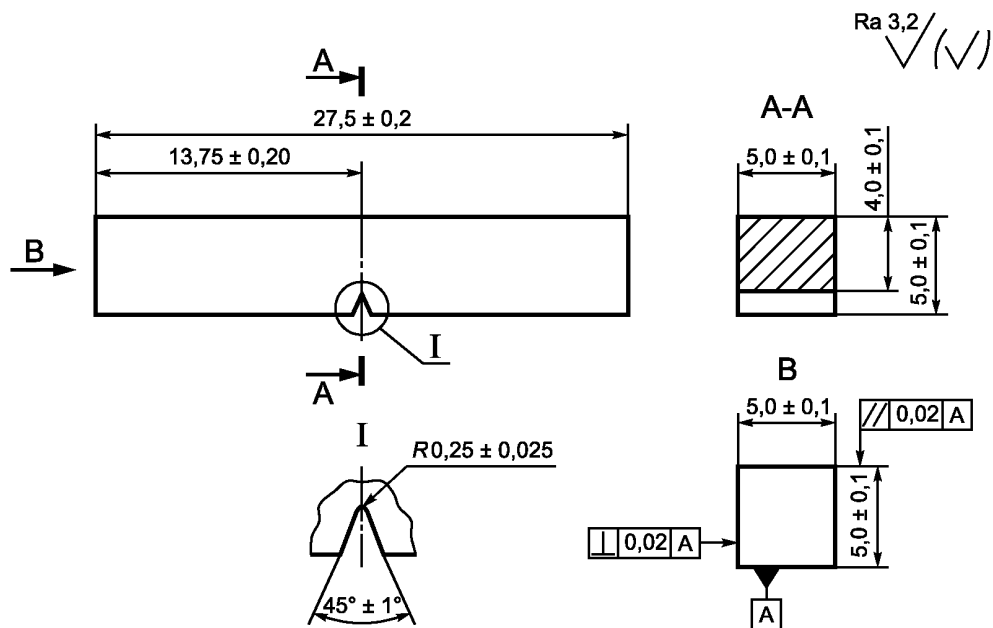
Малоразмерный образец размерами 5×5×27,5 мм для испытаний на ударный изгиб
